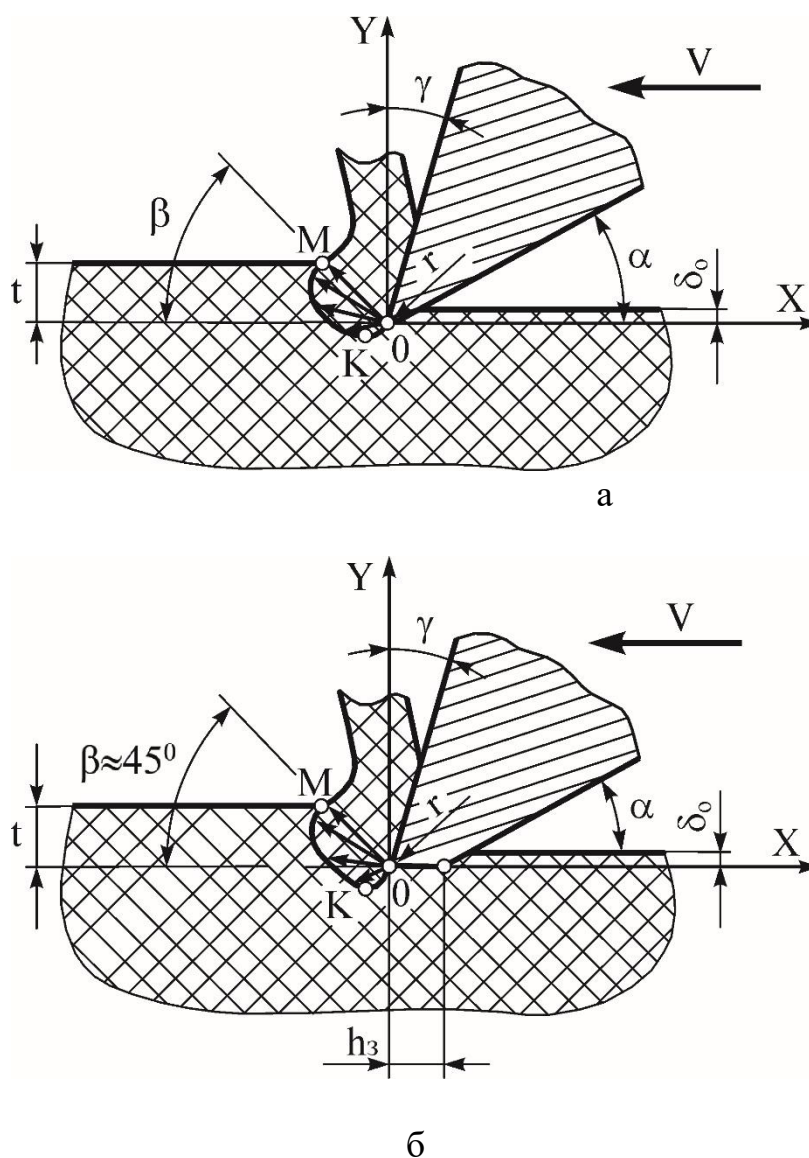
Зображення кінематичної схеми утворення стружки при лезвійній обробці полімерного композиту ріжучим клином: а – створення стружки незношеним різцем; б – створення стружки зі зношеним різцем
